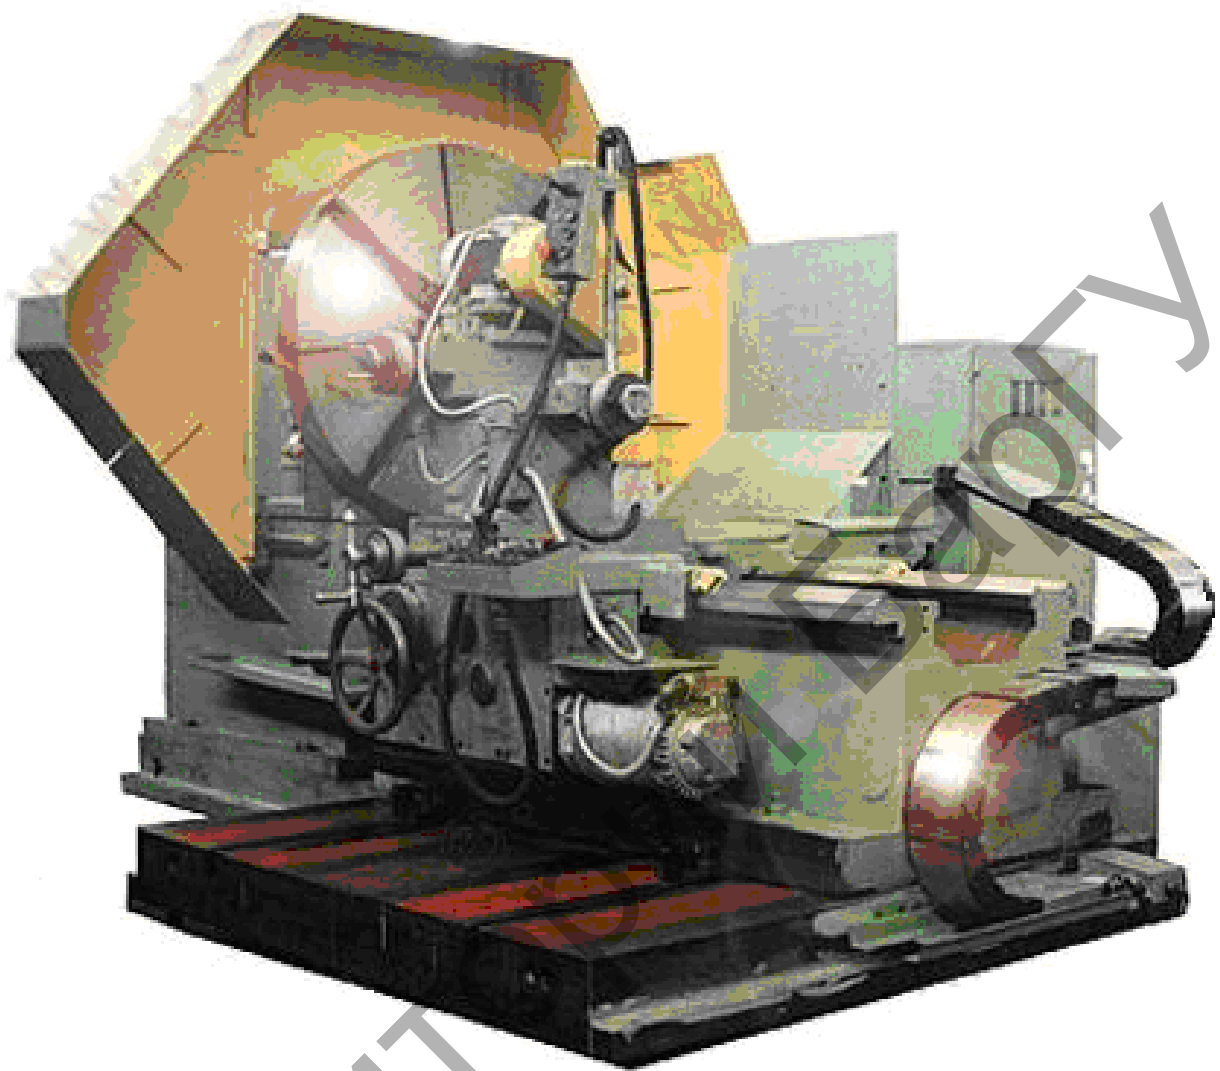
Токарно-лобовой станок модели 1P694
